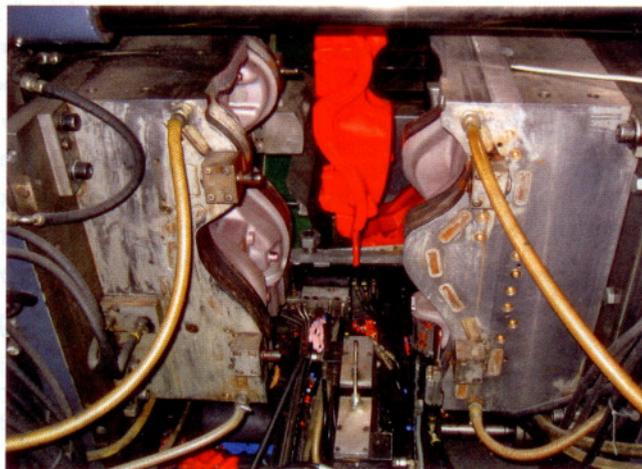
Das Bobby-Car am Ende der Kühlzeit beim Austrag aus dem Werkzeug
